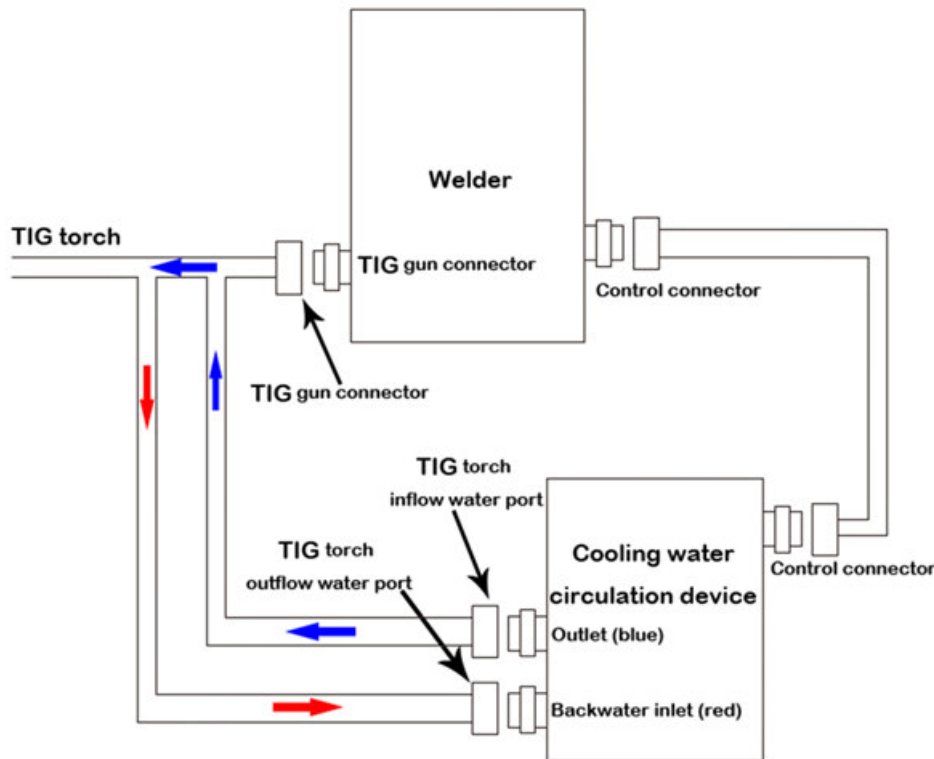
Anschlüsse an das Gerät für TIG-Schweißen
